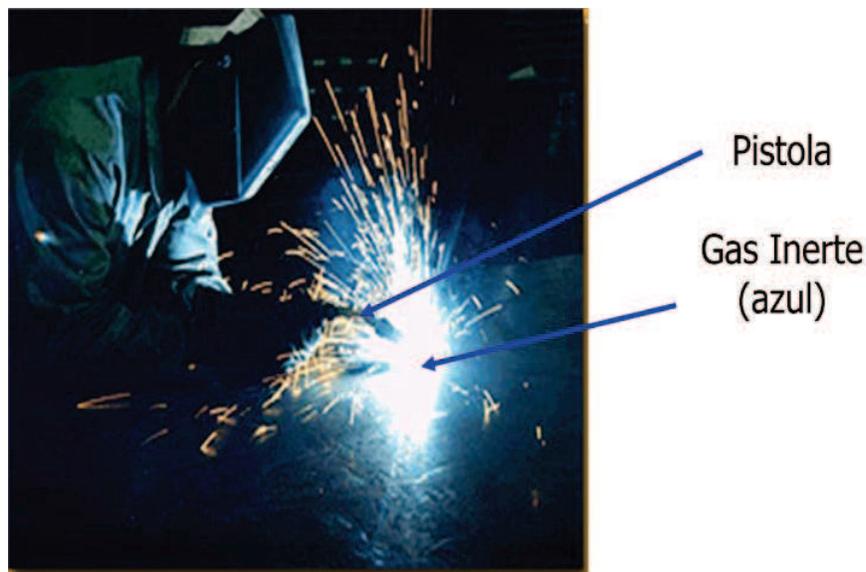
Proceso de Soldadura FCAW.
